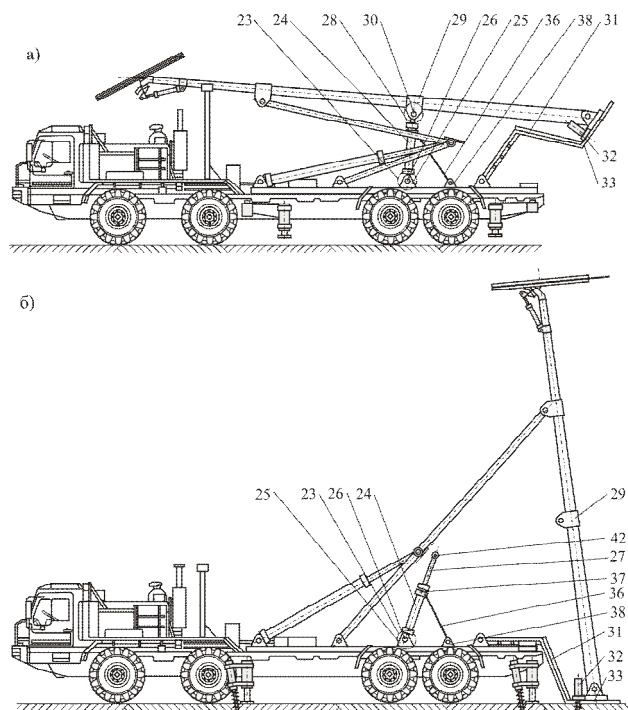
Общий вид самоходной машины (вид сбоку) с выносным расположением концевой опоры и складывающейся штангой (модификации Ву1-4/Х и Ву2-4/Х): а – транспортное положение концевой опоры; б – рабочее положение концевой опоры
